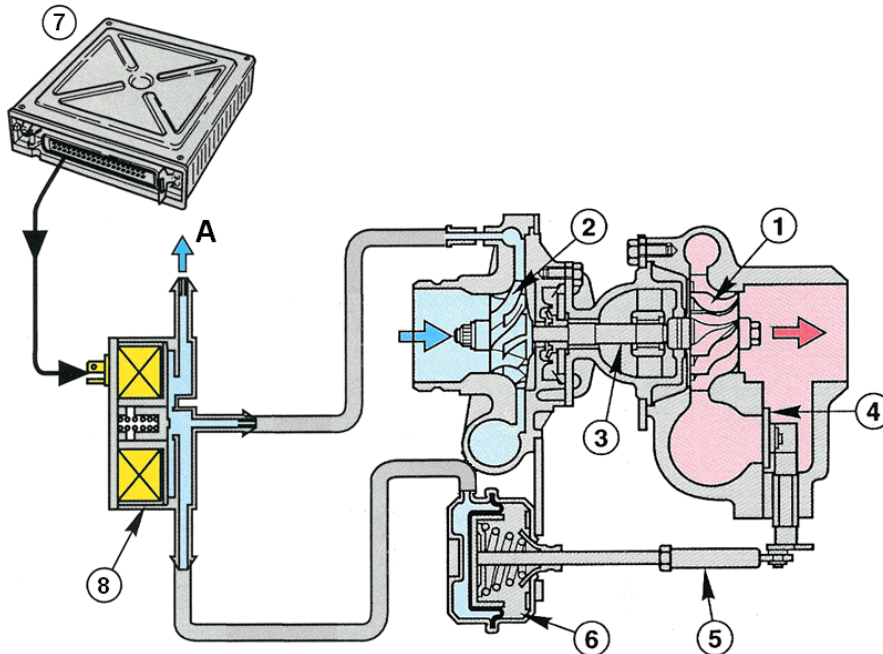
Abgasturbolader mit Bypass (Wastegate) mit elektronischer Ladedruckregelung durch das Motorsteuergerät. A = Leckluft; 1 = Turbinenrad; 2 = Verdichterrad; 3 = Verbindungswelle; 4 = Klappenventil; 5 = Druckstange; 6 = Membrandose; 7 = Motorsteuergerät; 8 = Magnetregelventil.
